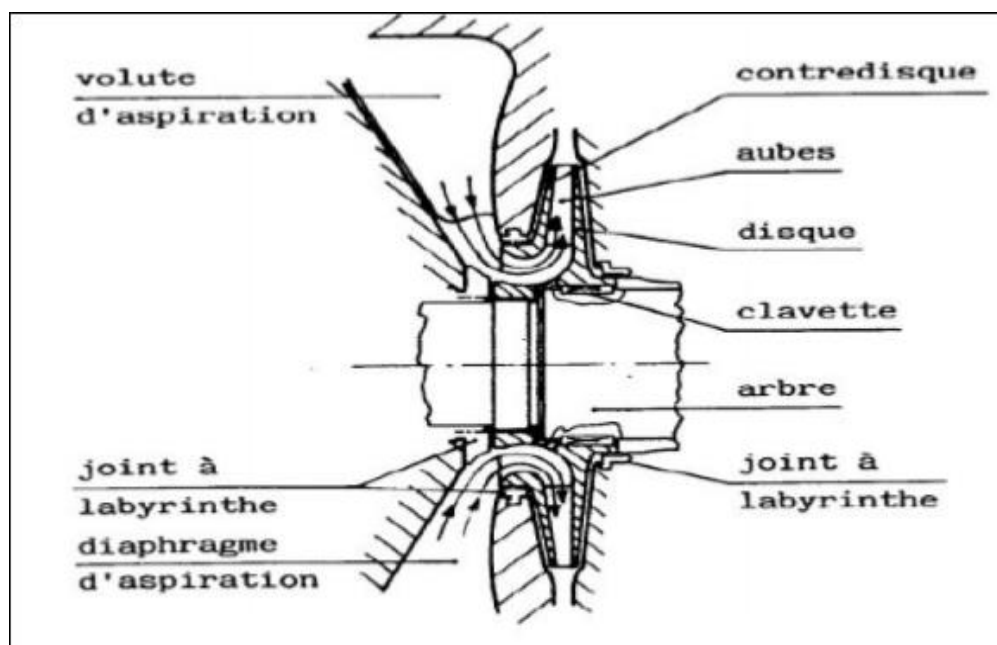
Vue latérale de la roue d'un compresseur centrifuge.
